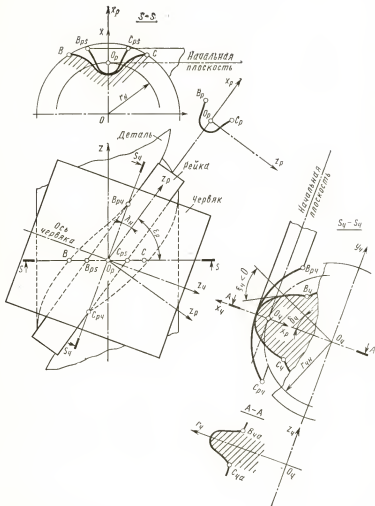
Схема для определения профиля основного червяка, сопрягающегося с зубчатой деталью
